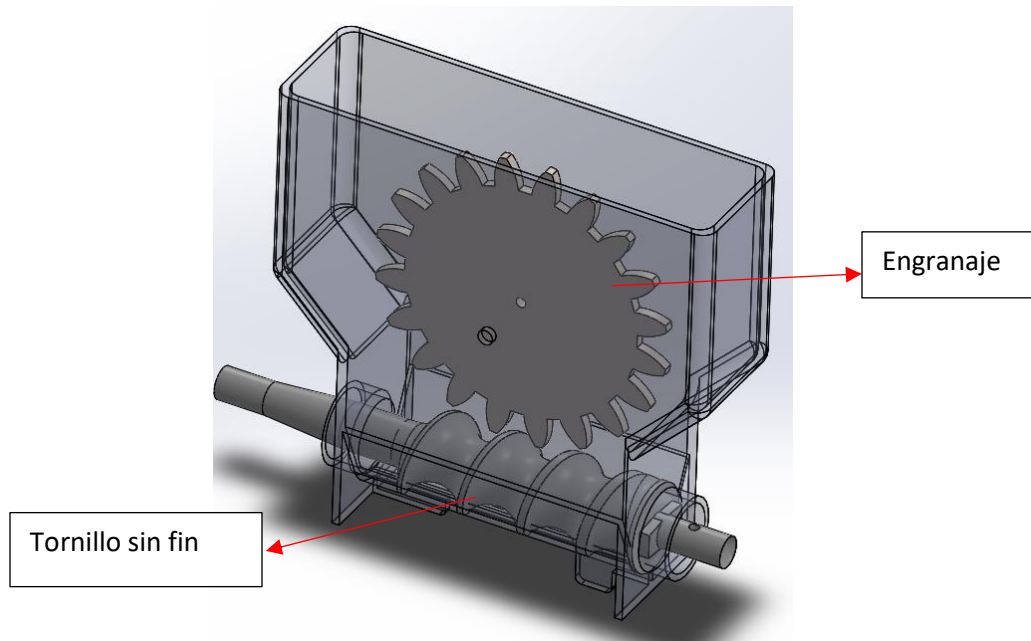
14. Tornillo sin fin más engranaje. Fuente: Autoría propia
